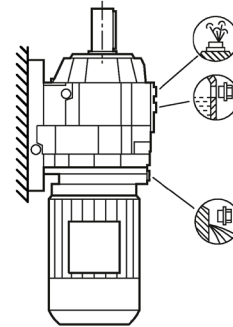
Einbaulagen für Stirnradgetriebe D/Z Fußausführung Baugrößen 19 - 29
